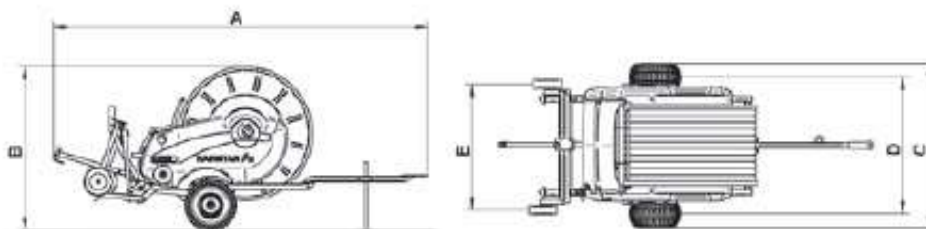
Schema ansamblu instalație tambur și furtun [123]
